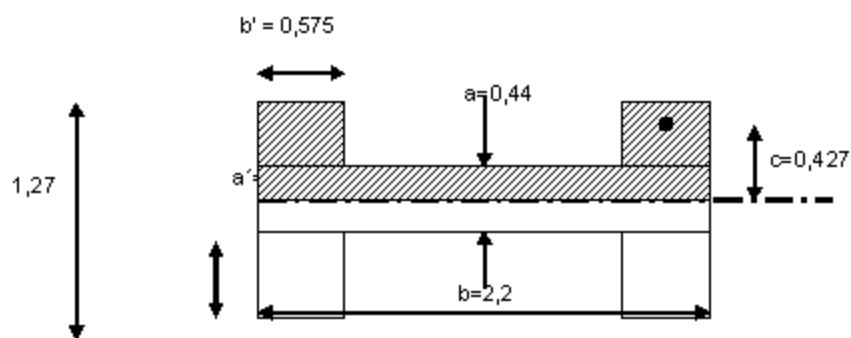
Sección Transversal Biela Chevrolet Corsa
